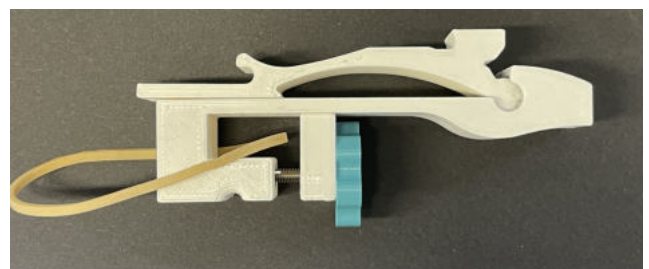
Die kürzere Schraube wird am Rumpf befestigt.
